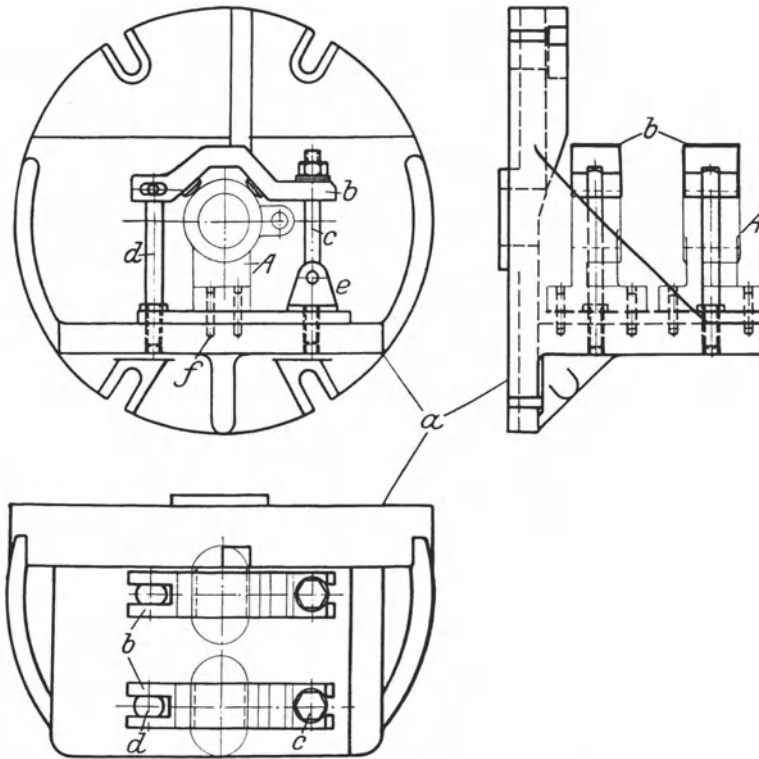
Aufspannvorrichtung für Zugsindellager.
